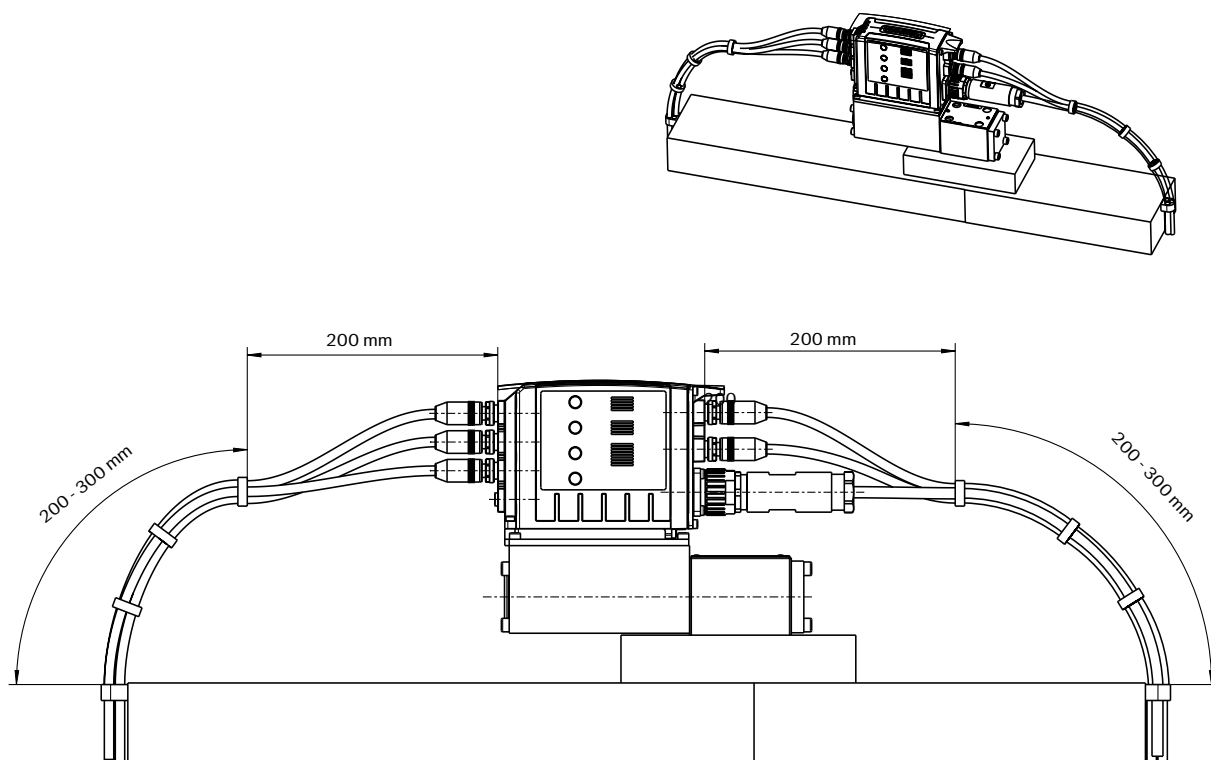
Beispiel für die Montage und Verlegung der M12-Stecker und Kabel
